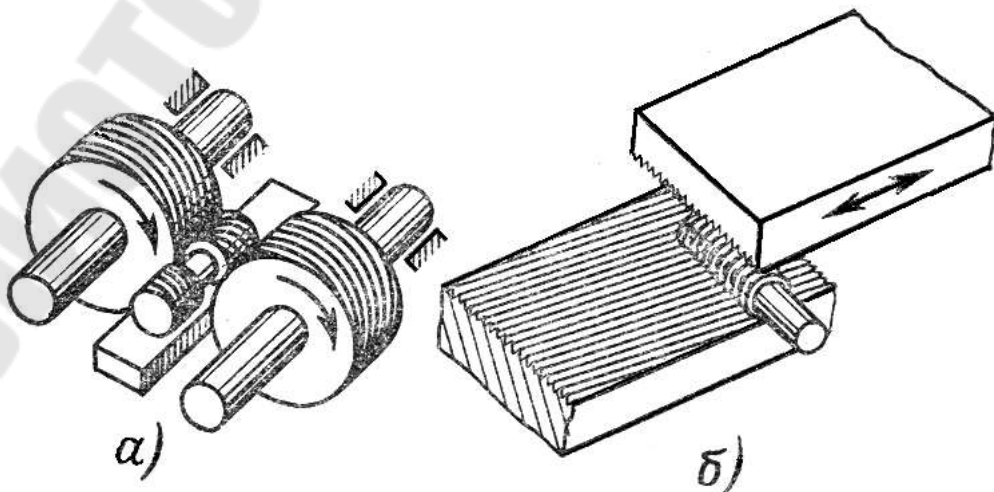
Схемы накатывания резьбы: *a* – роликами; *б* – плашками
